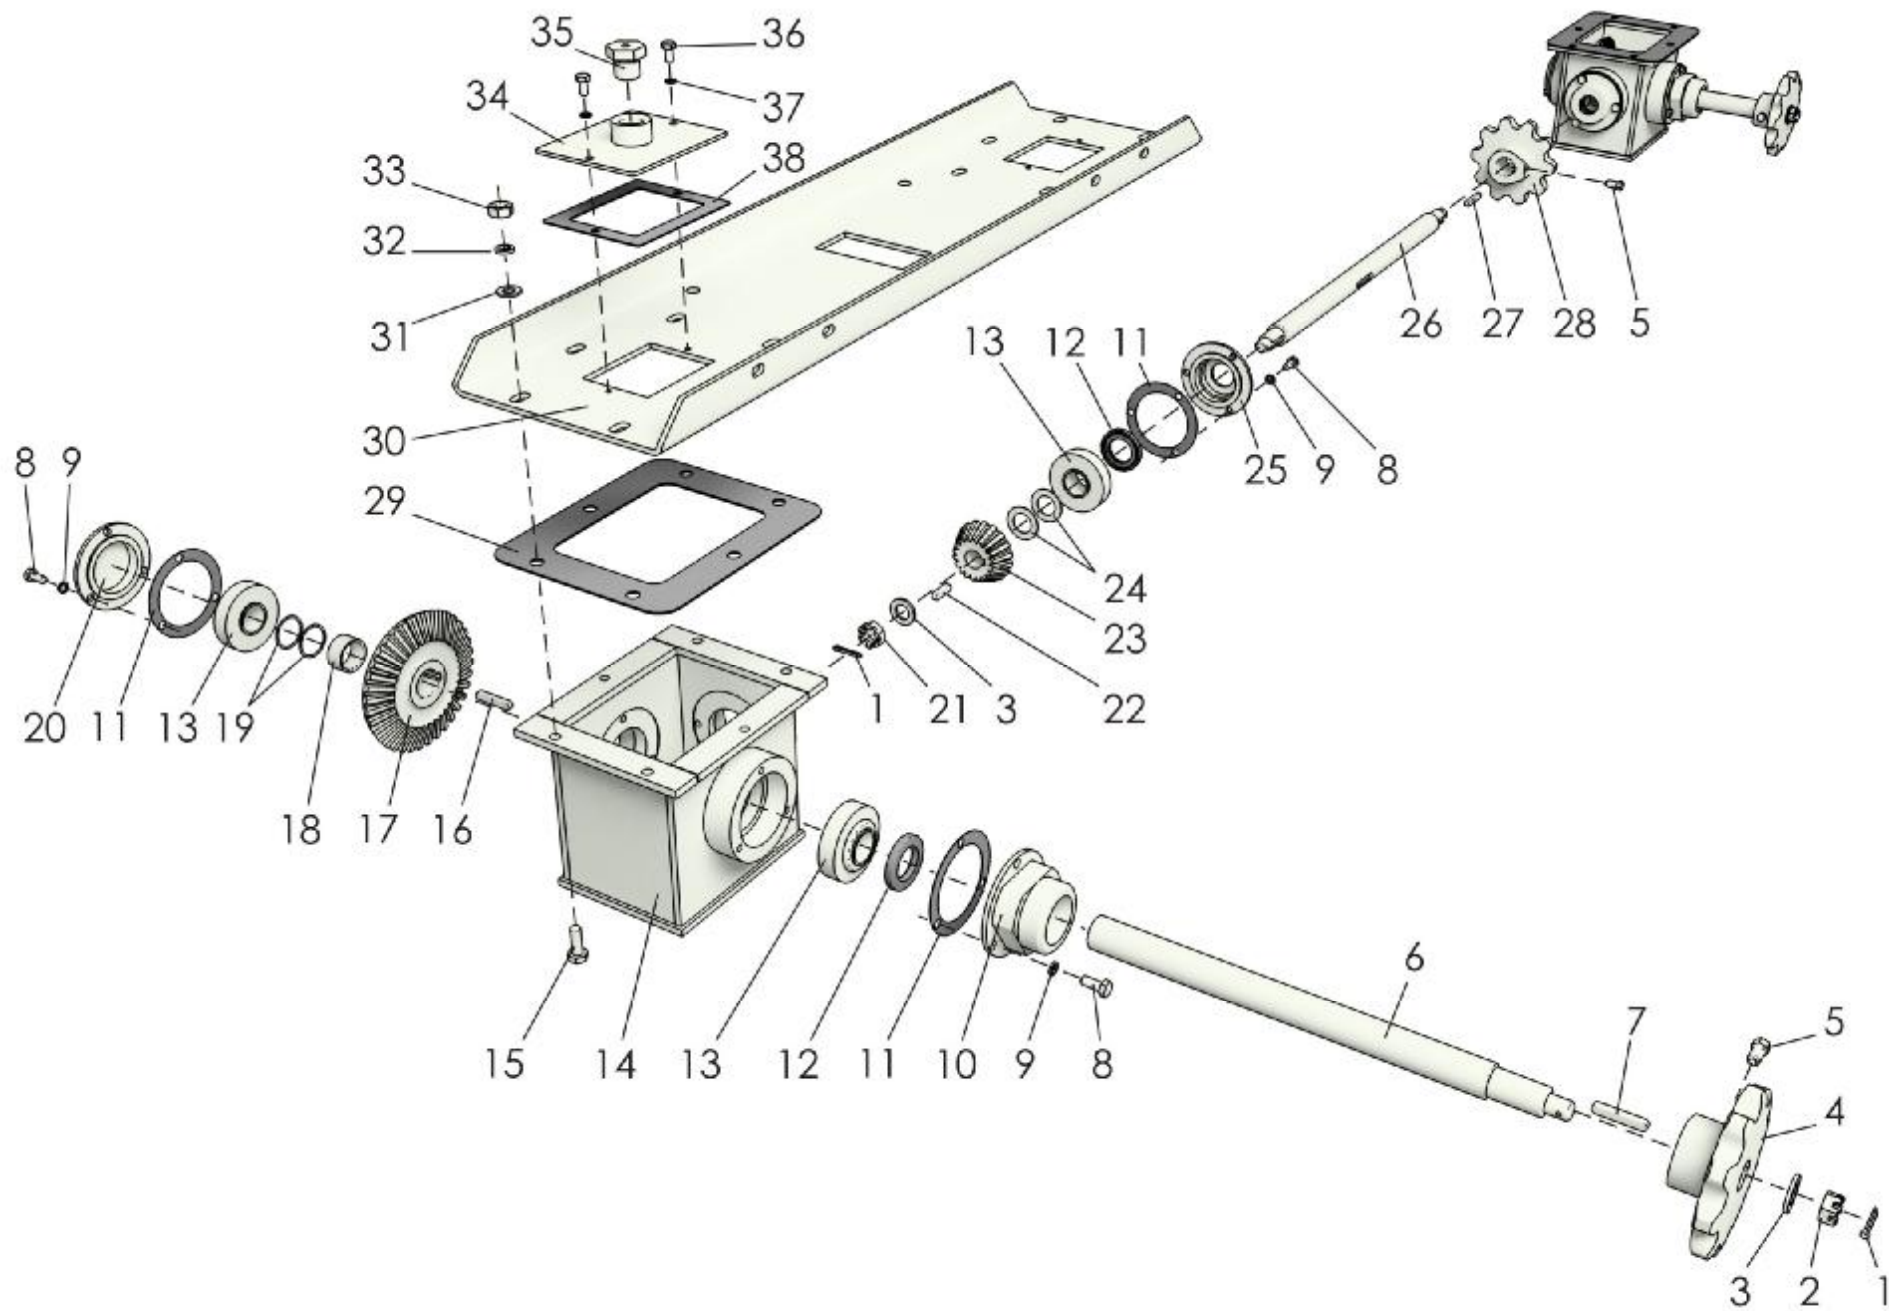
Крышка со сварными редукторами МЗС-90.03.050
